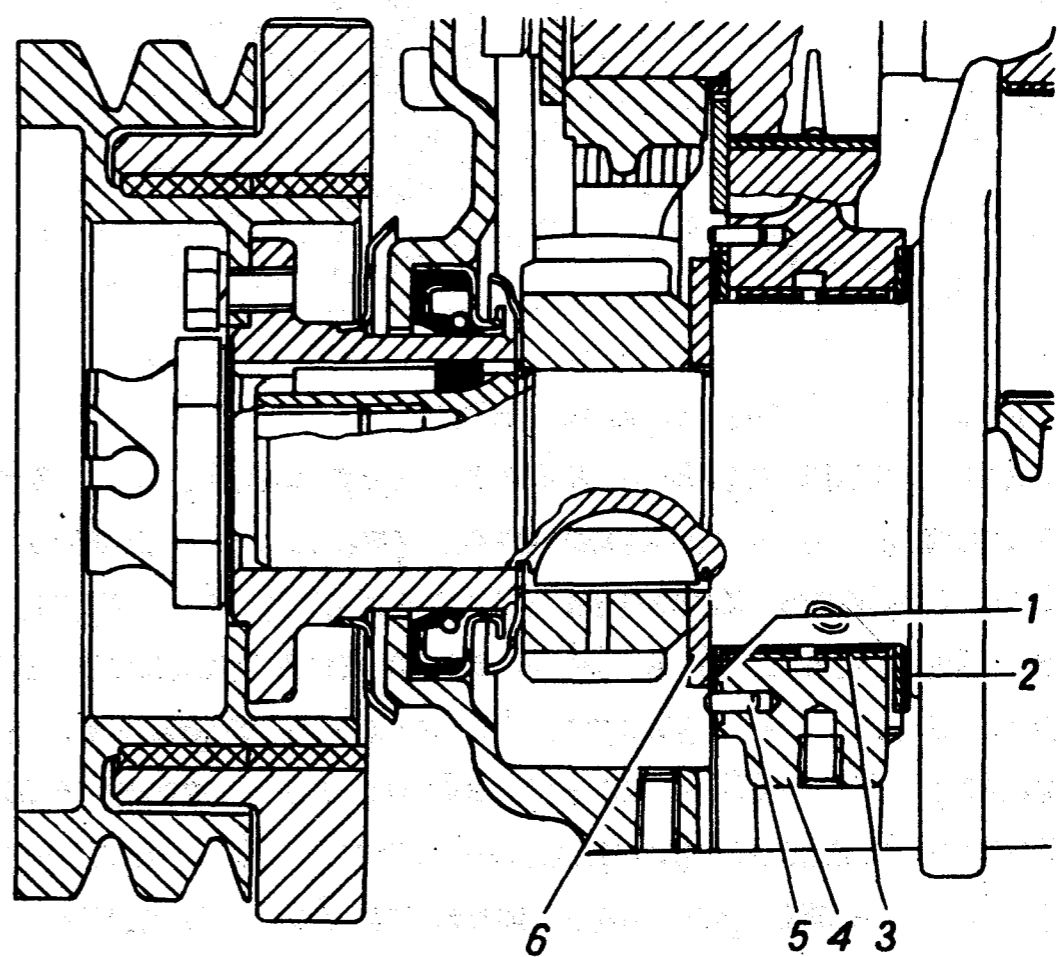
Передний конец коленчатого вала: 1 и 2 — шайбы упорные; 3 — вкладыш подшипника; 4 — крышка подшипника; 5 — штифт; 6 — шайба
